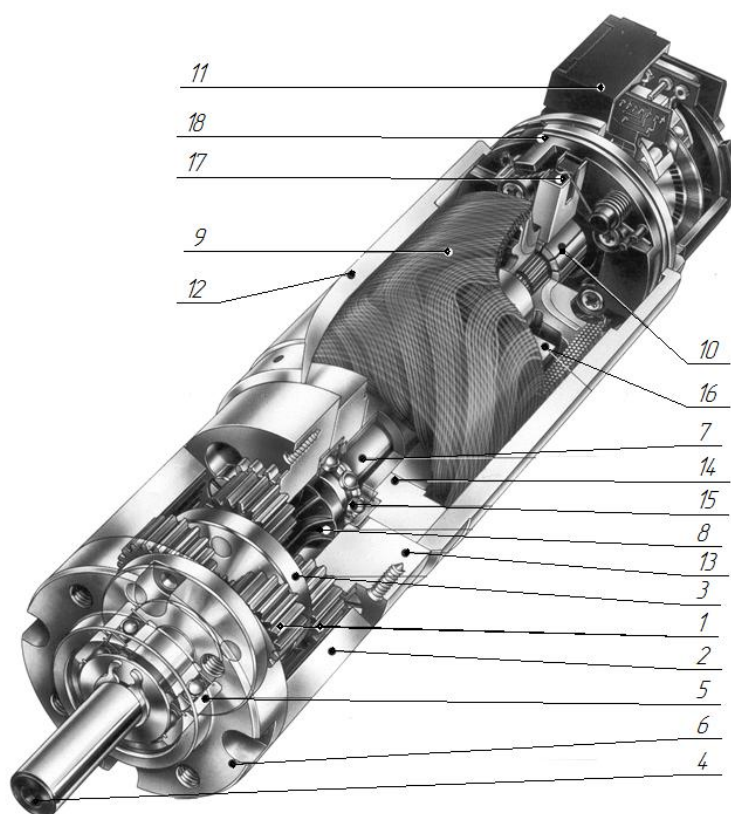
Сервопривод фирмы «maxon motor ag»
